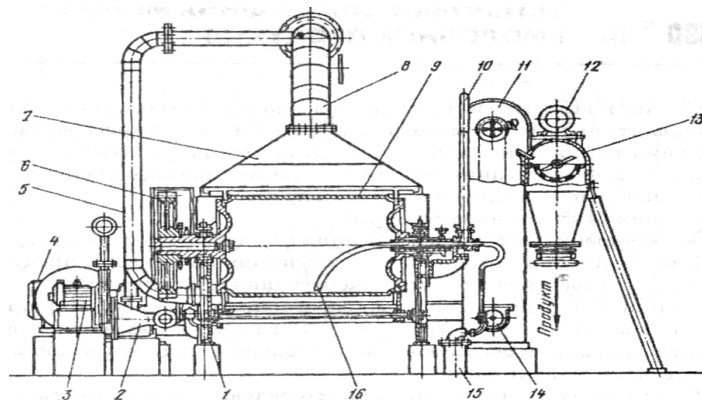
Сушильно-подрібнювальний агрегат СДА—250:
